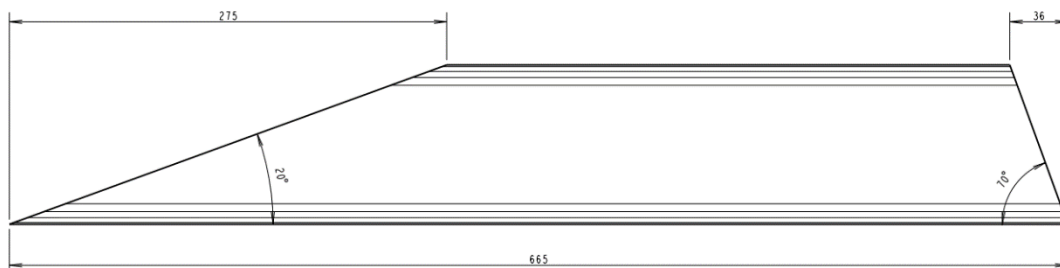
Refuerzo de parachoques, viga de acero A36 UPN 100 de 630 mm
